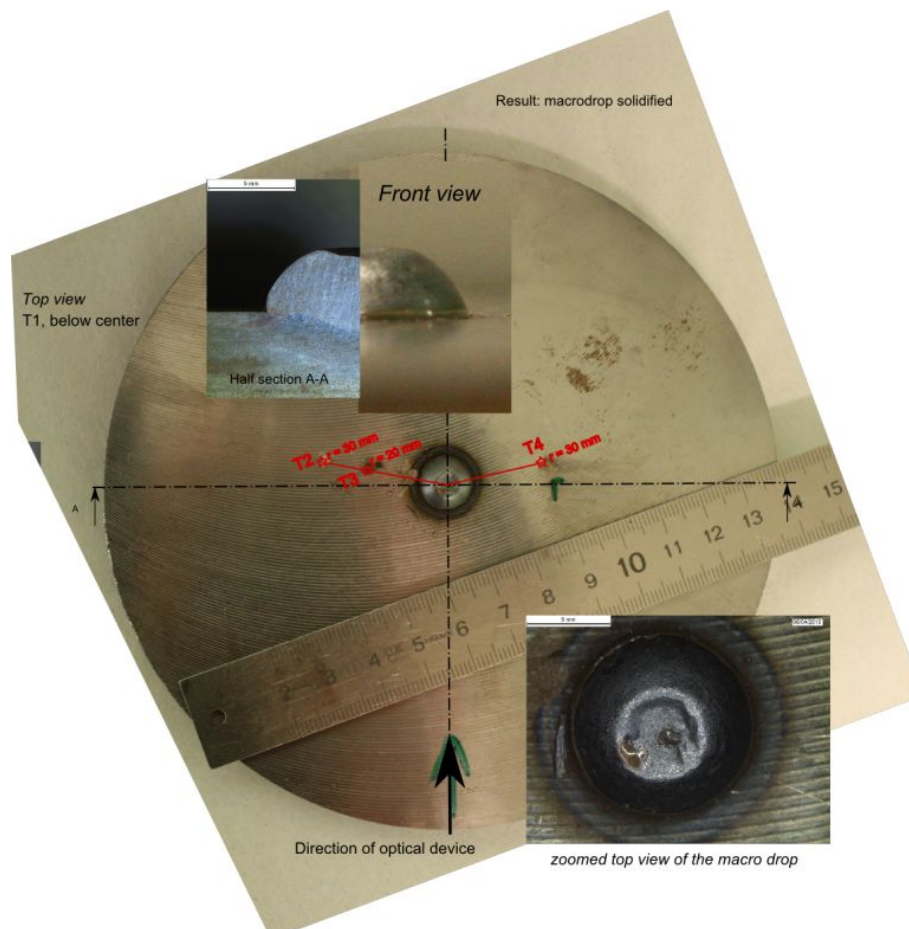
Vue générale des éprouvettes après essais et détails de la macro-goutte (macrographie et vue de dessus)
